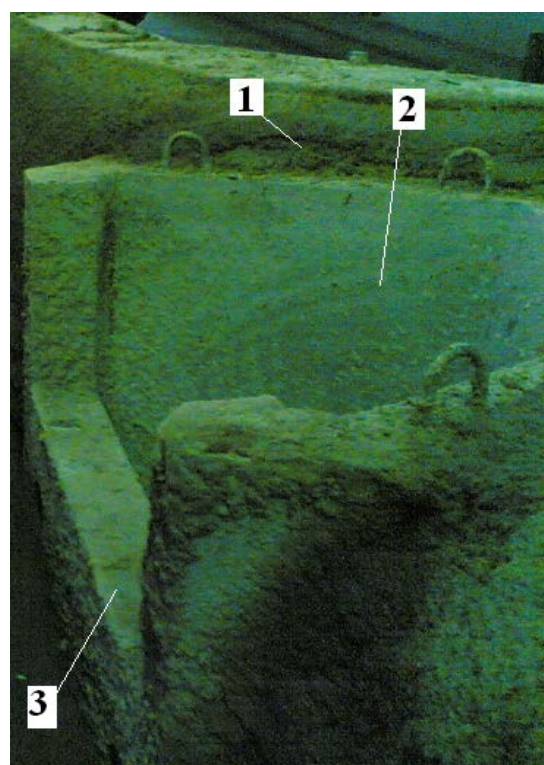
Модуль для защиты приемной камеры при подаче стали в приемную камеру промежуточного ковша: 1 – борт приемной камеры; 2 – защитное устройство; 3 – порог для защиты разливочного отверстия
